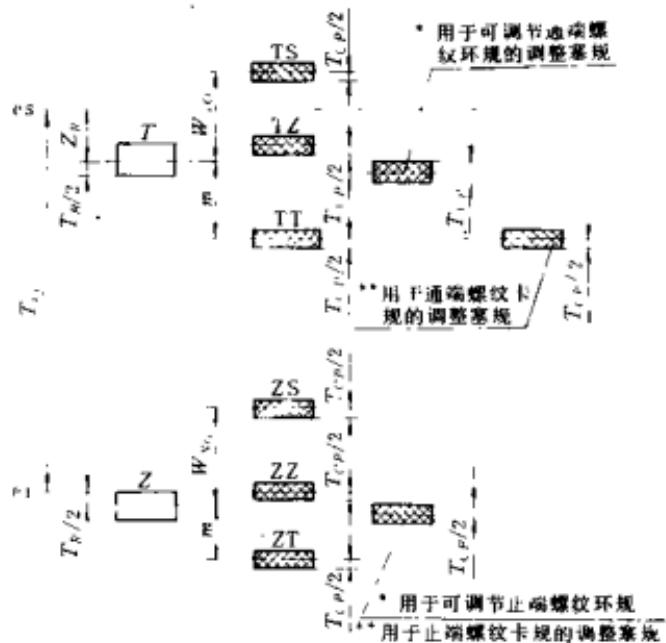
检验工件外螺纹用螺纹量规中径公差带图
